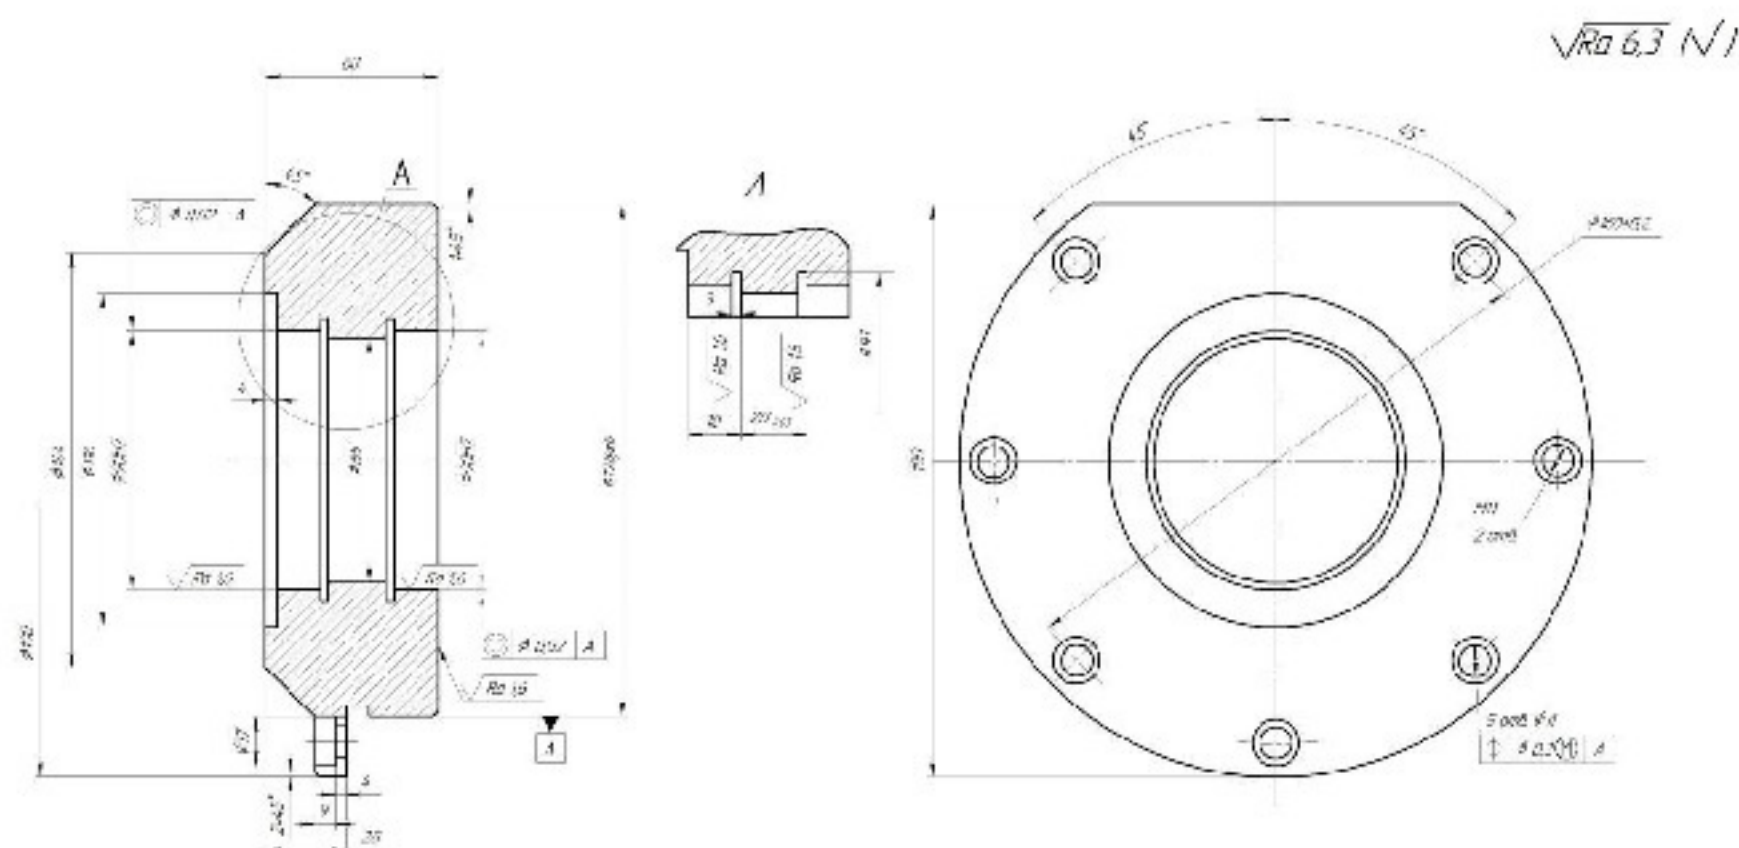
Креслення типової деталі типу «Стакан»
